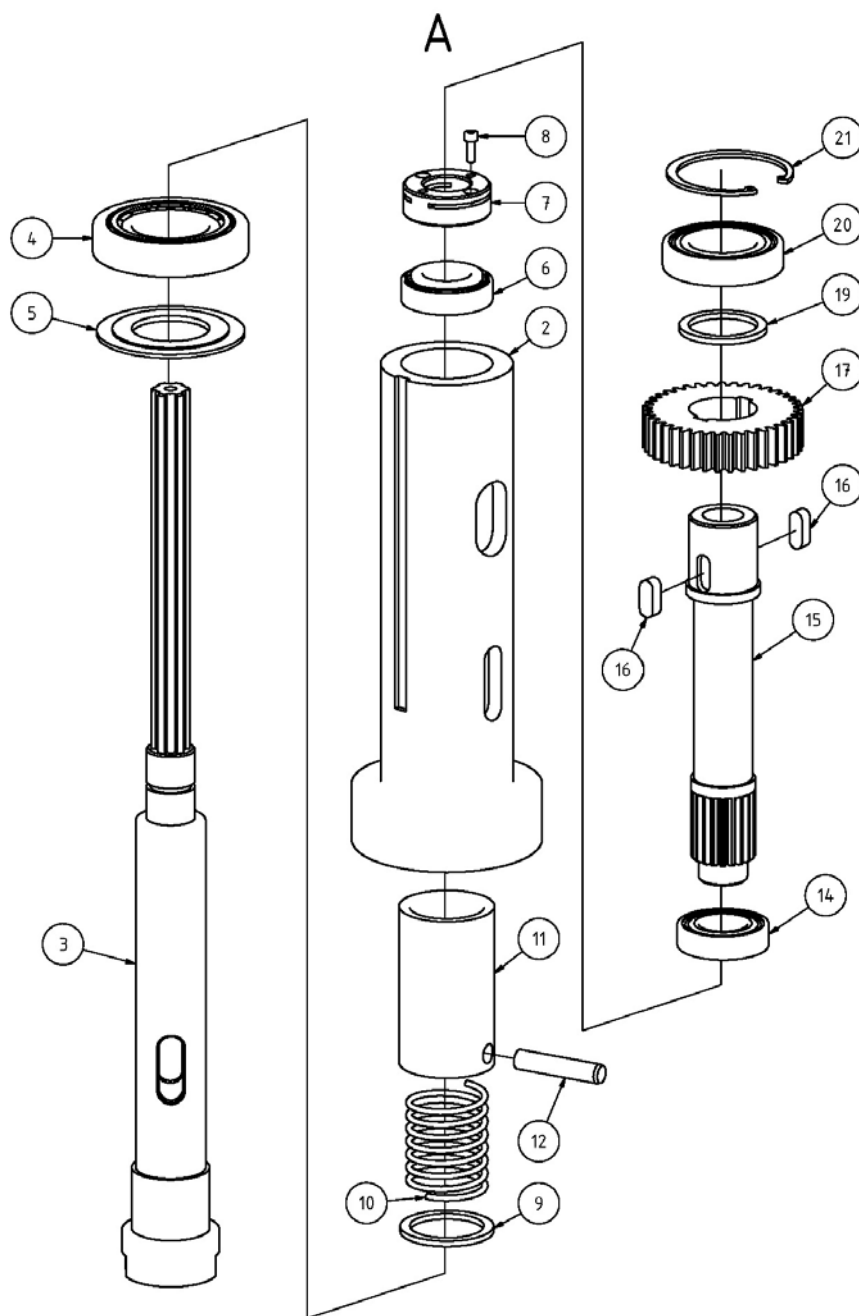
Bohrkopf 1 von 6 - Cabezal taladrador 1 de 6
